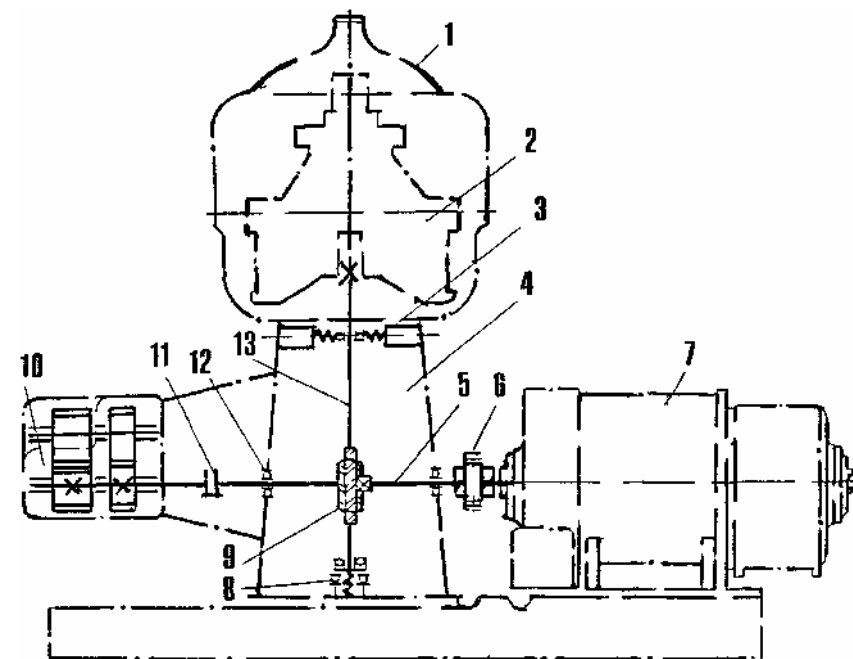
Принципиальная кинематическая схема сепаратора. 1 - сборник; 2 - барабан; 3 - верхняя опора; 4 - станина; 5 - горизонтальный вал; 6 - фрикционная муфта; 7 - электродвигатель; 8 - нижняя опора; 9 - червячно-винтовая пара; 10 - шестеренные насосы; 11 - эластичная муфта; 12 - подшипник; 13 - вертикальный вал.
